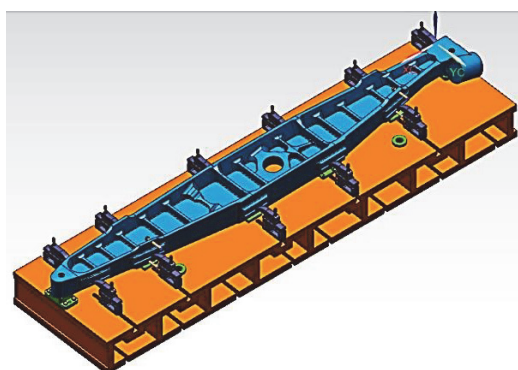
Заготовка «шассийной балки» в приспособлении
